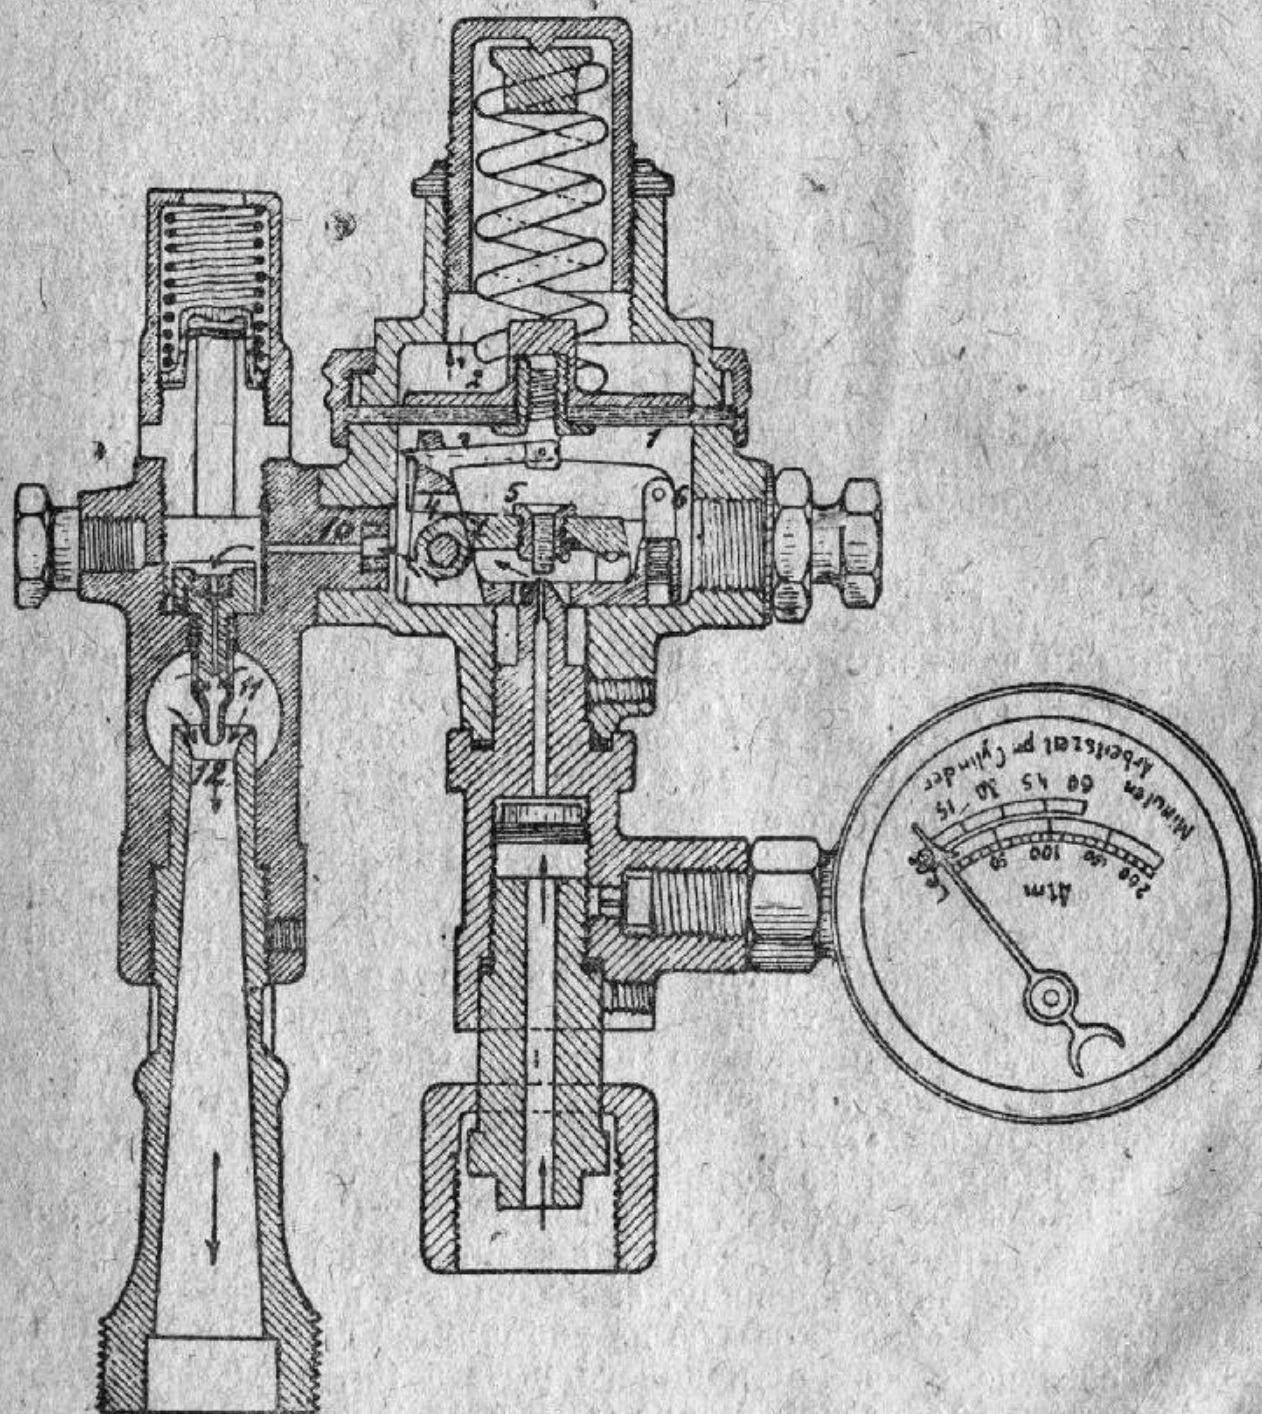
Инжектор, редукционный и предохранительный клапаны и манометр респиратора Дрегера 1904—1909 гг.
